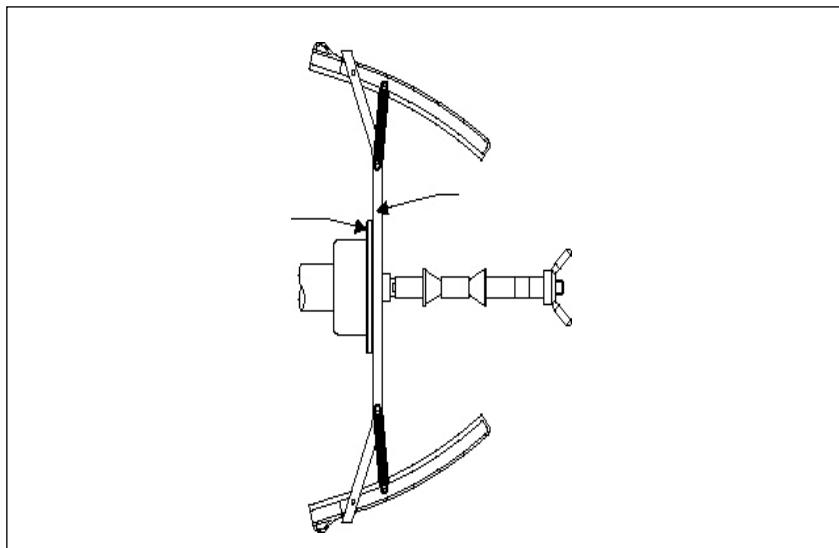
Installieren Sie die Klemmen auf der Auswuchtwelle. Richten Sie die "Gewindelöcher" an Klemmen mit den "Befestigungslöchern" an der Auswuchtwelle aus.
